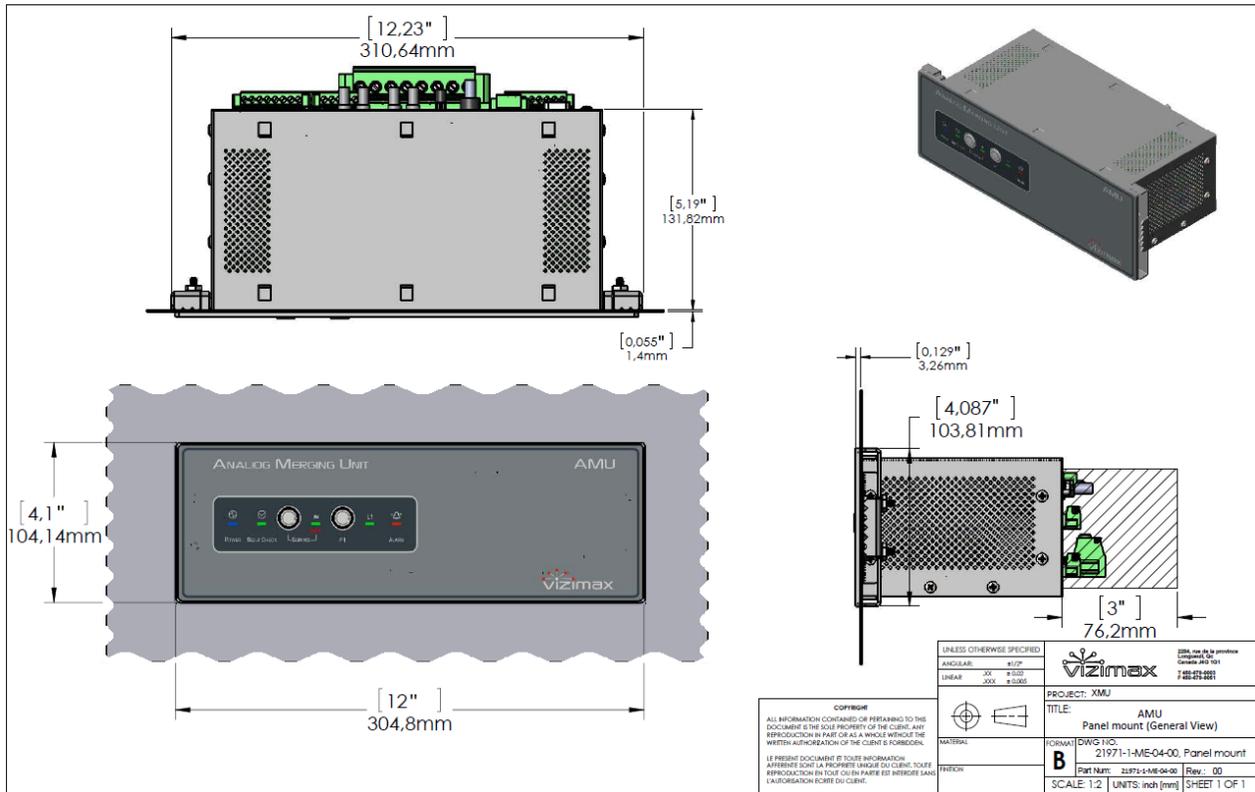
CONFIGURATION POUR MONTAGE SUR PANNEAU
